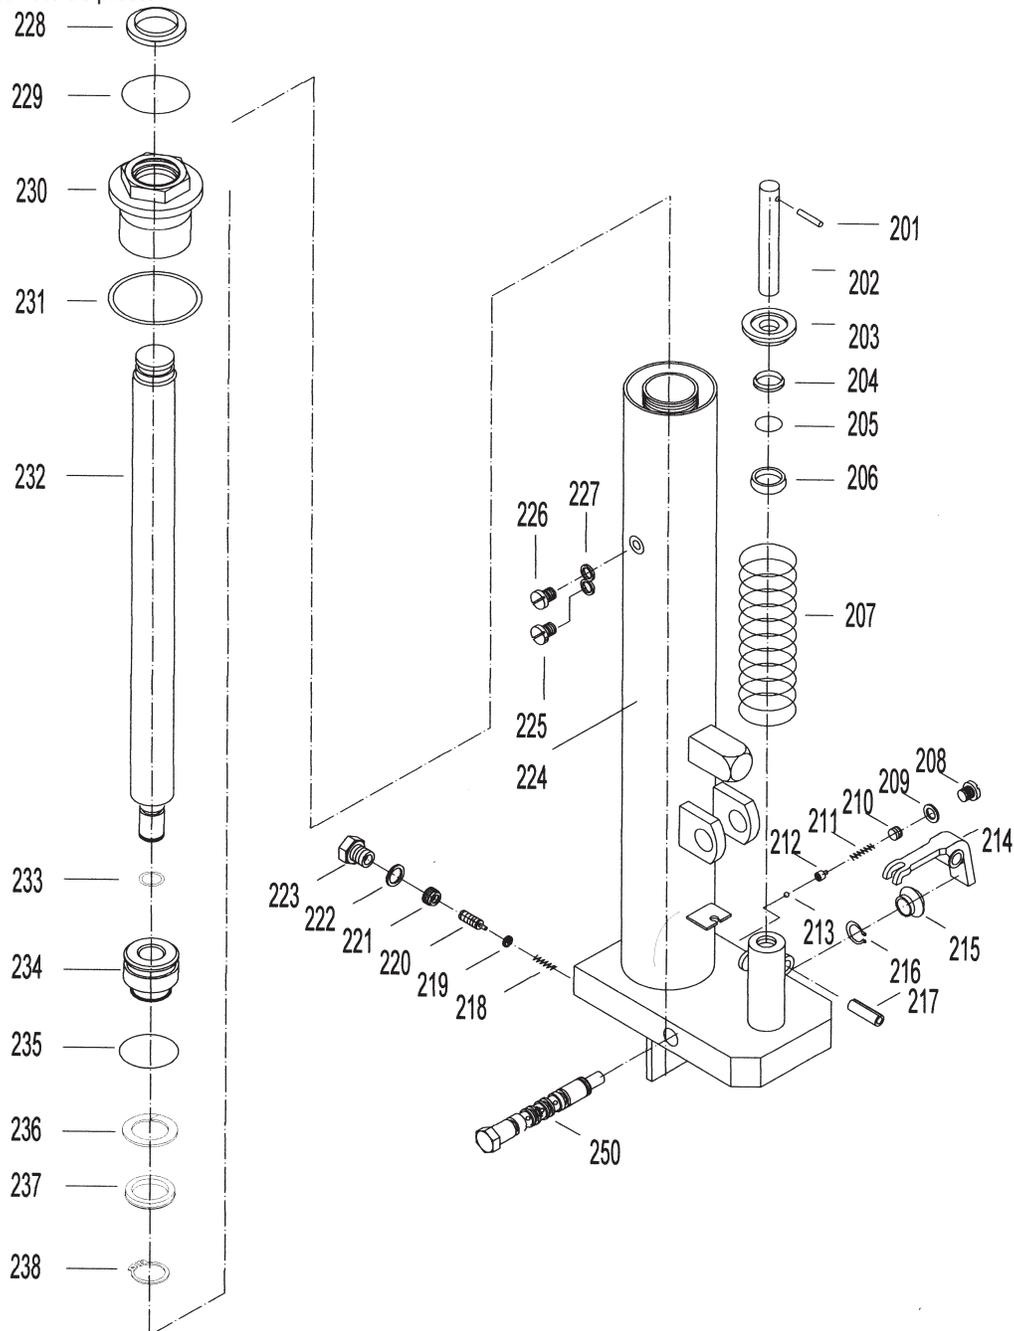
Illustration des pièces détachées pour 11K273 et 11K276, Pompe hydraulique
